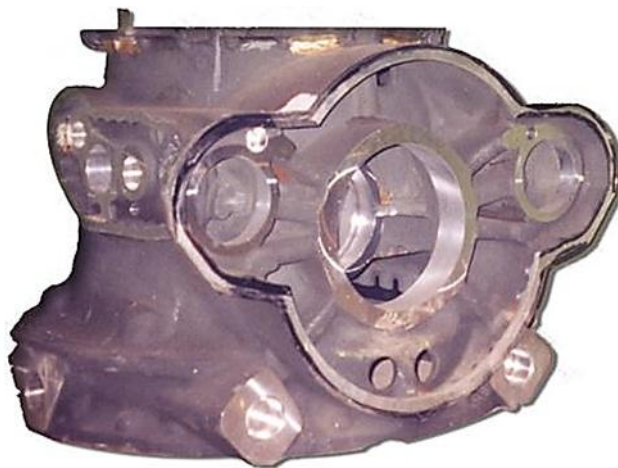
Корпус редуктора из магниевого сплава МЛ5
